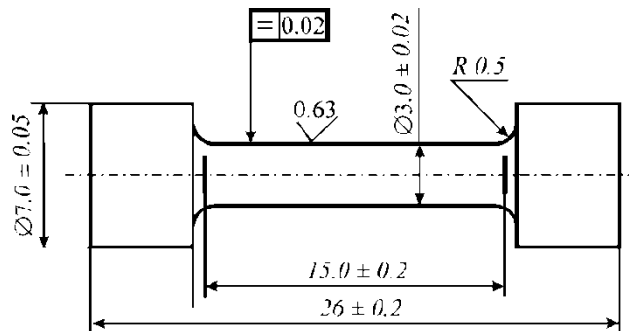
Эскиз цилиндрического образца из плавки 192031
